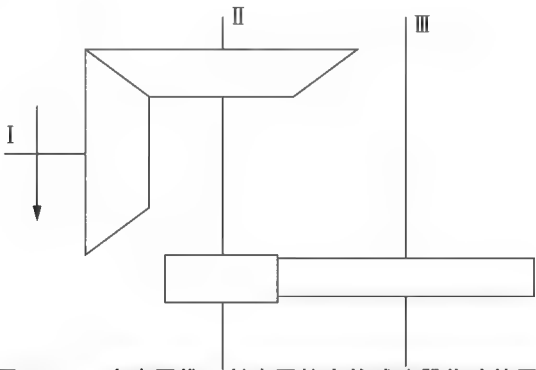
直齿圆锥—斜齿圆柱齿轮减速器传动简图
